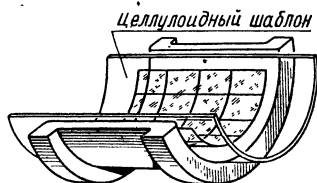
Проверка качества шабрения внутренних поверхностей вкладышей и подшипников скольжения целлулоидным шаблоном
